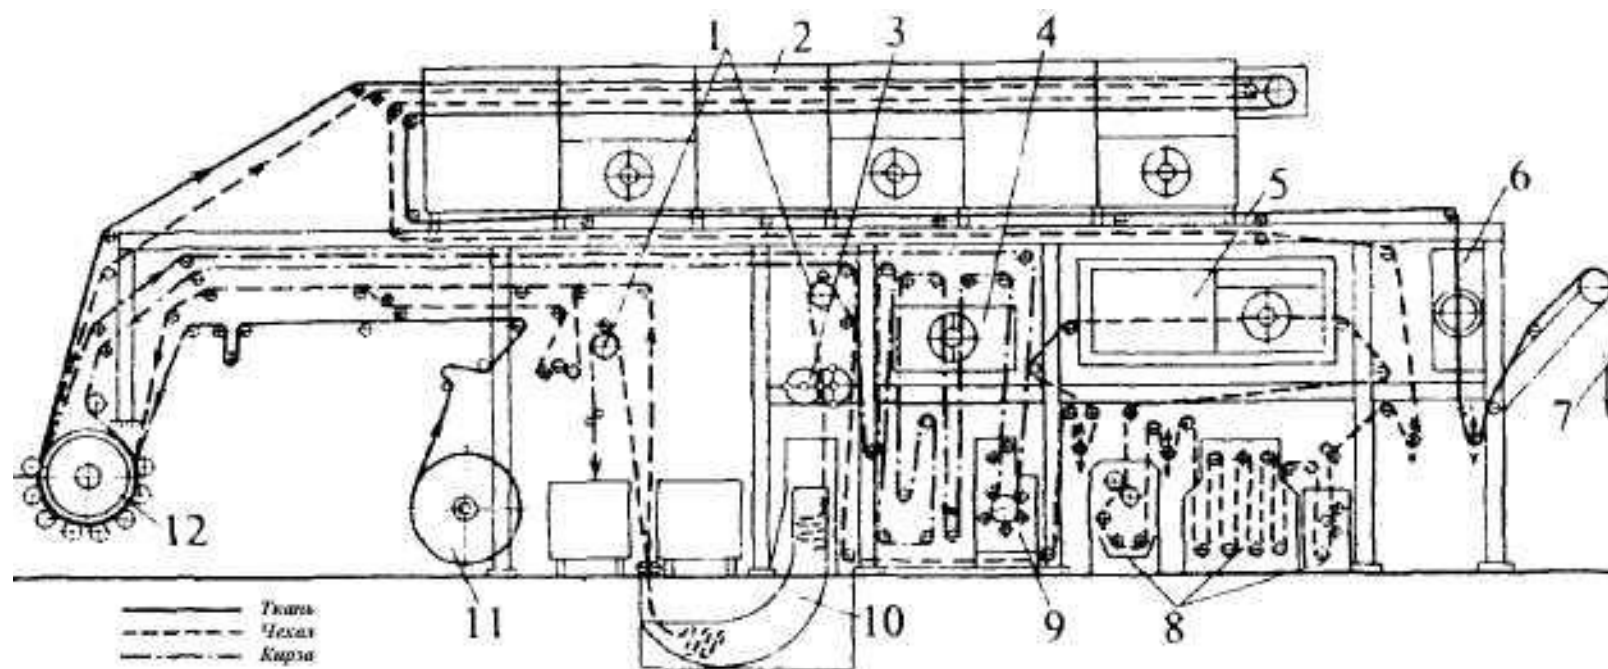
Тканепечатный агрегат с гравированными печатными валами
